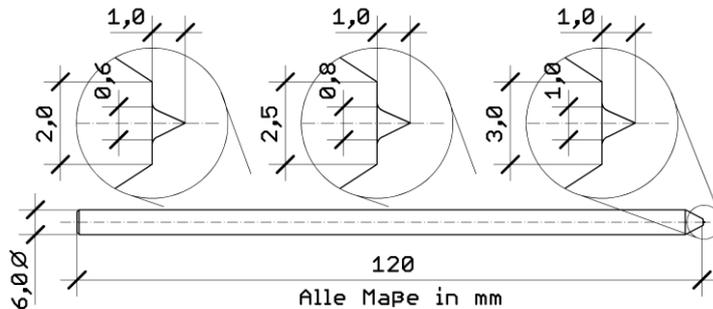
Primitives Werkzeug zum Setzen der Rohrnieten
